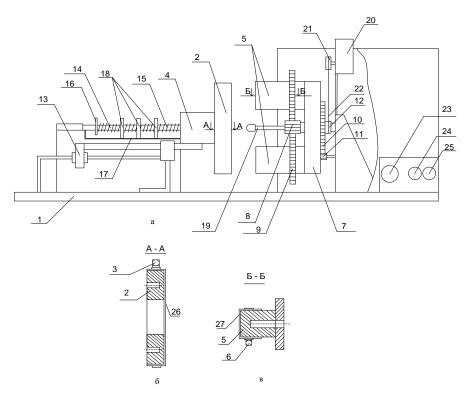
кинематическая схема устройства — общий вид (а), съемный держатель испытуемого образца материала (б), съемный истирающий элемент (в).
